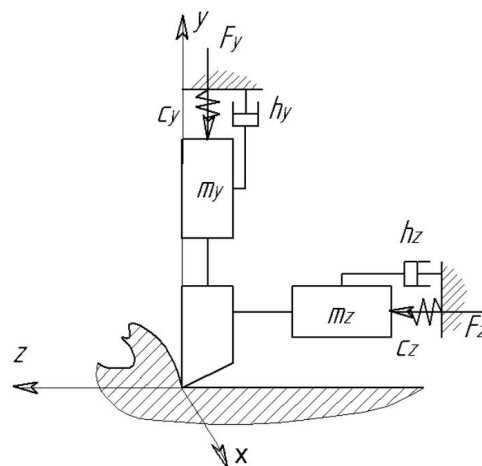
Модель обробної системи торцевого фрезерування з обмеженими автоколиваннями [145]
